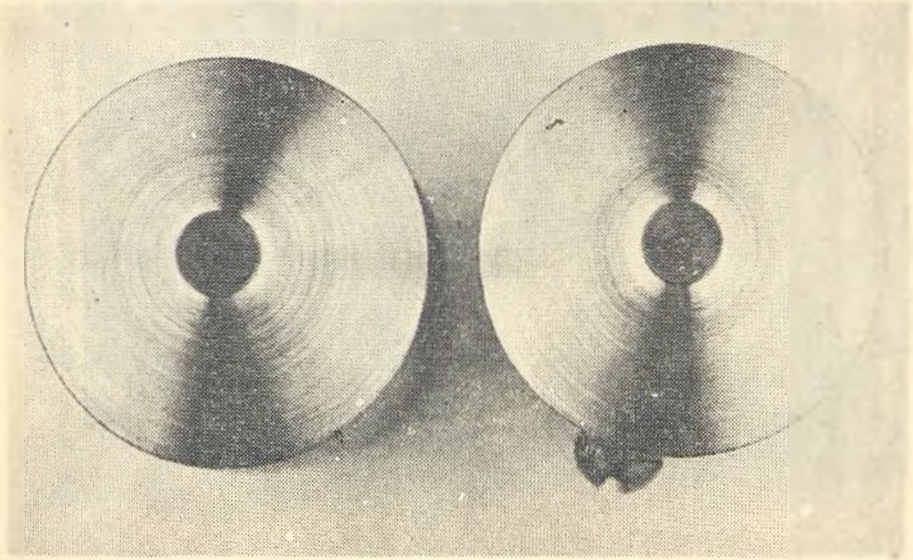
Schweisselektrodenpaar (Form B).
